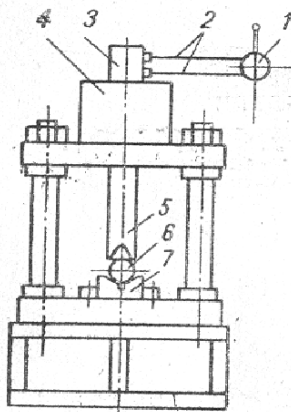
Схема пневматического пресса правки и рихтовки прутков.
